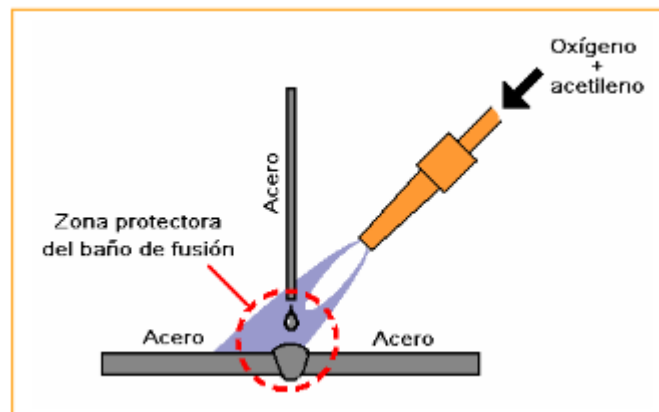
Soldadura Oxiacetilénica [11]
